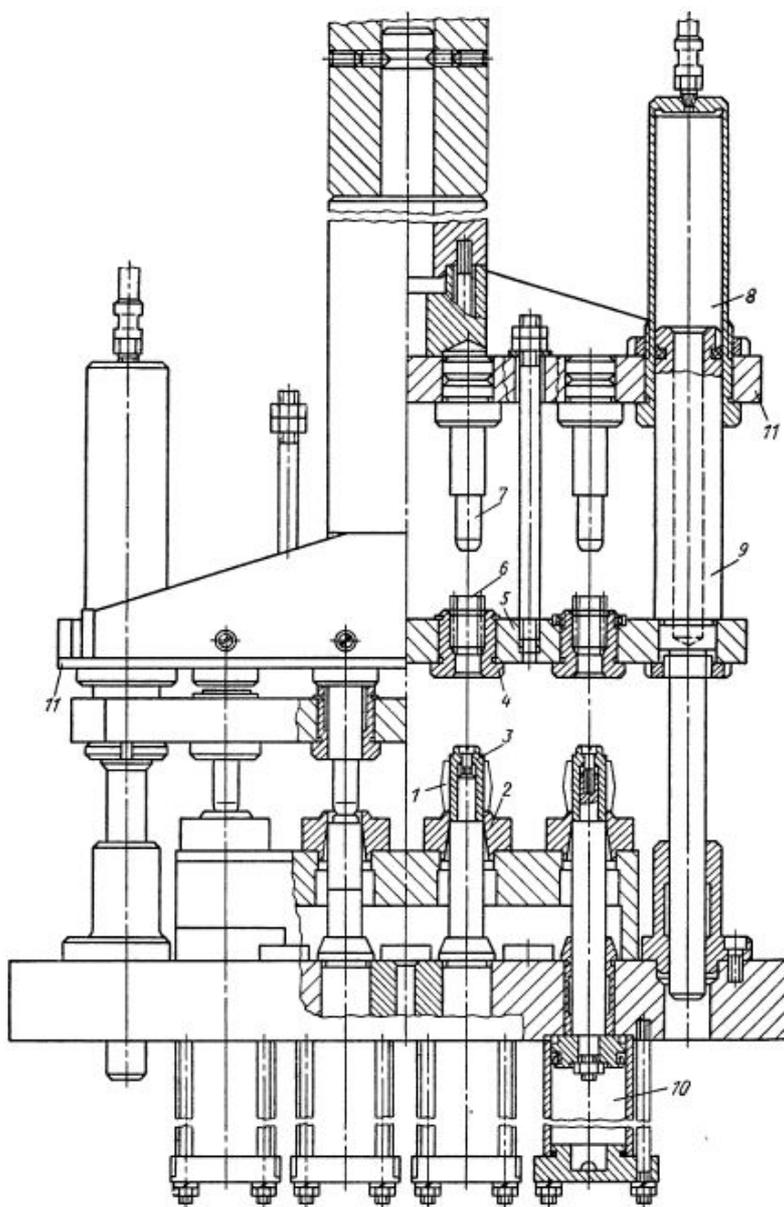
Схема запрессовки втулок в коромысла клапанов
